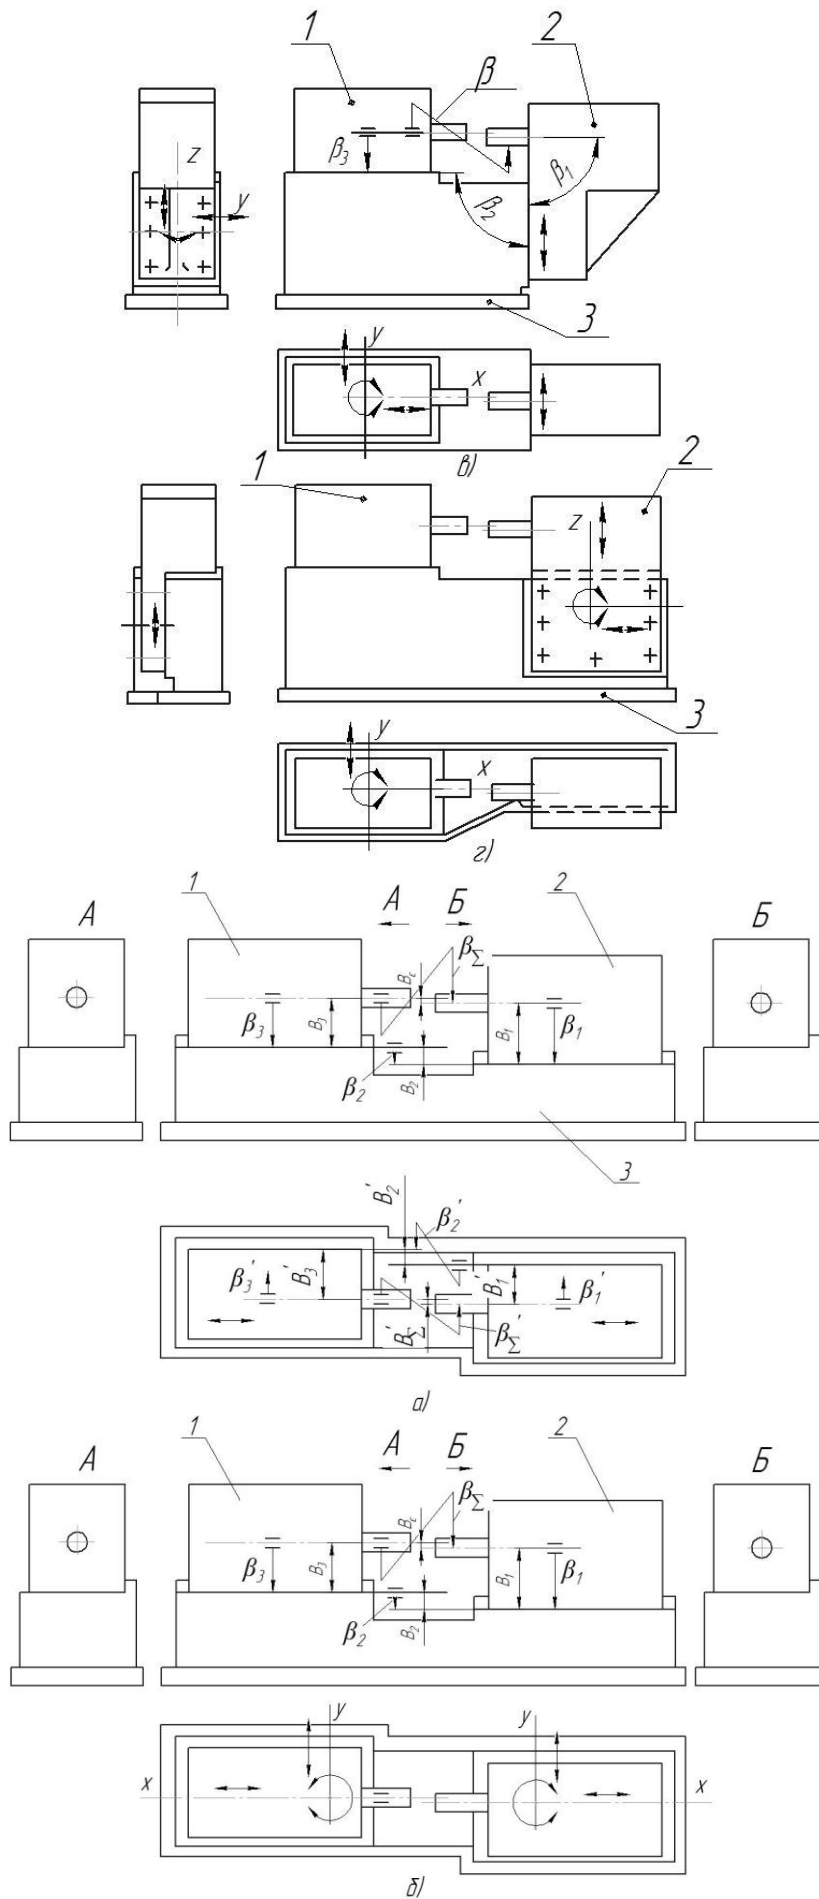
Схема розрахунку допусків при компонованні обладнання
